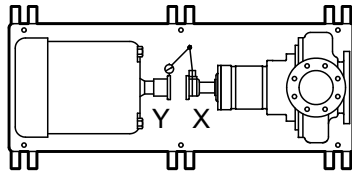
Vista dall'alto di un allineamento orizzontale scorretto
